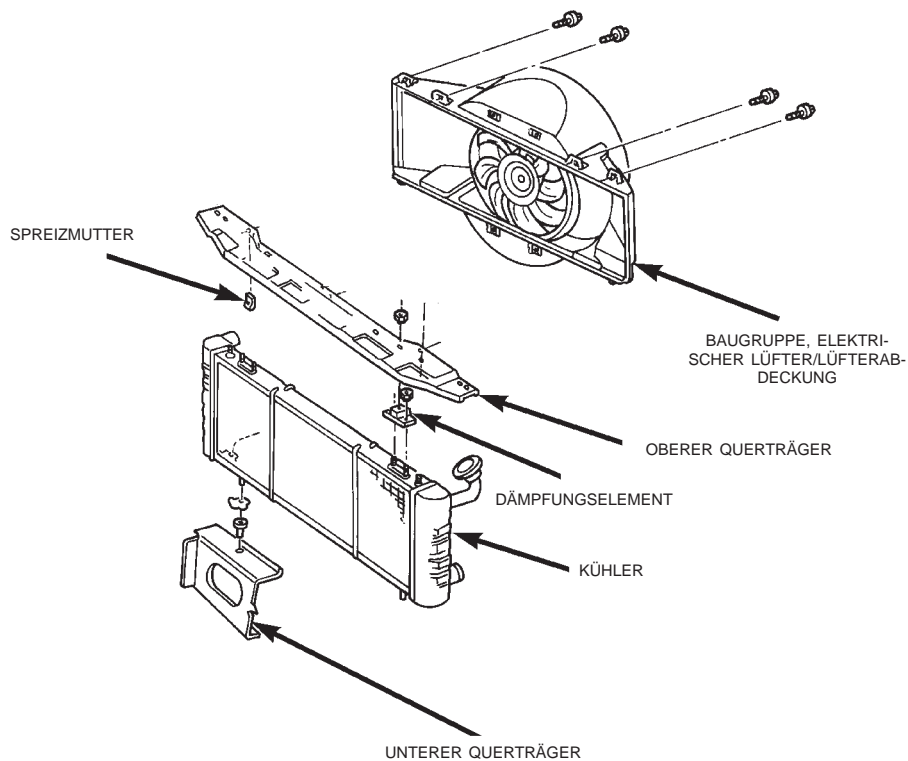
Aus-/Einbau des Kühlers—2.5L-Motor
